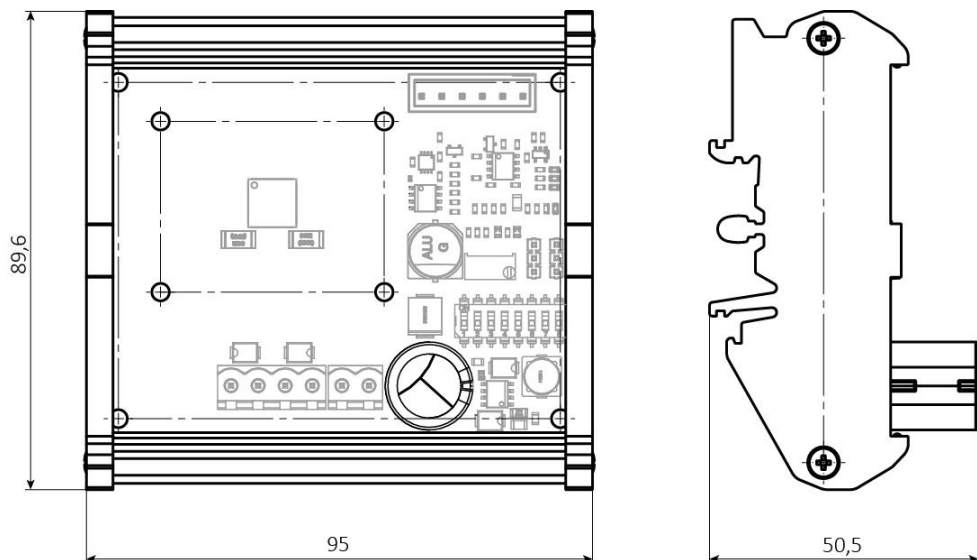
Габаритные и присоединительные размеры драйвера шагового двигателя
